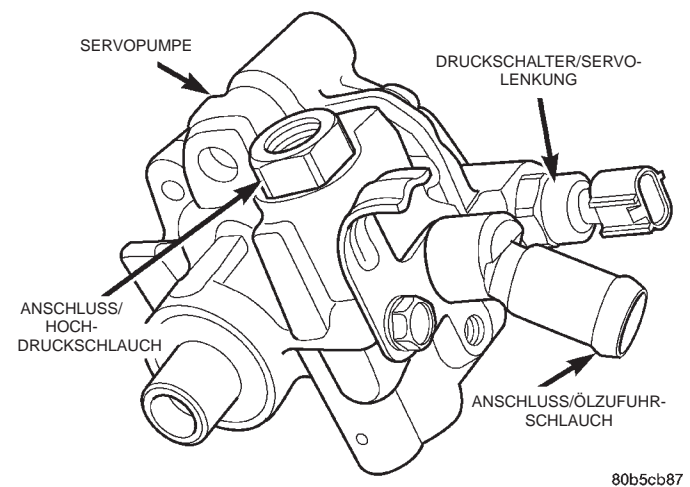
Anordnung des Druckschalters/Servolenkung bei Fahrzeugen mit 3.2L-/3.5L-Motor
